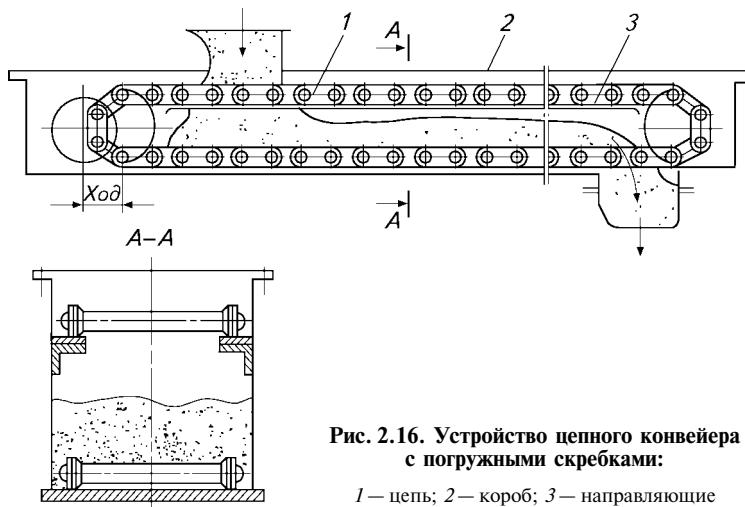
Устройство цепного конвейера с погружными скребками:
